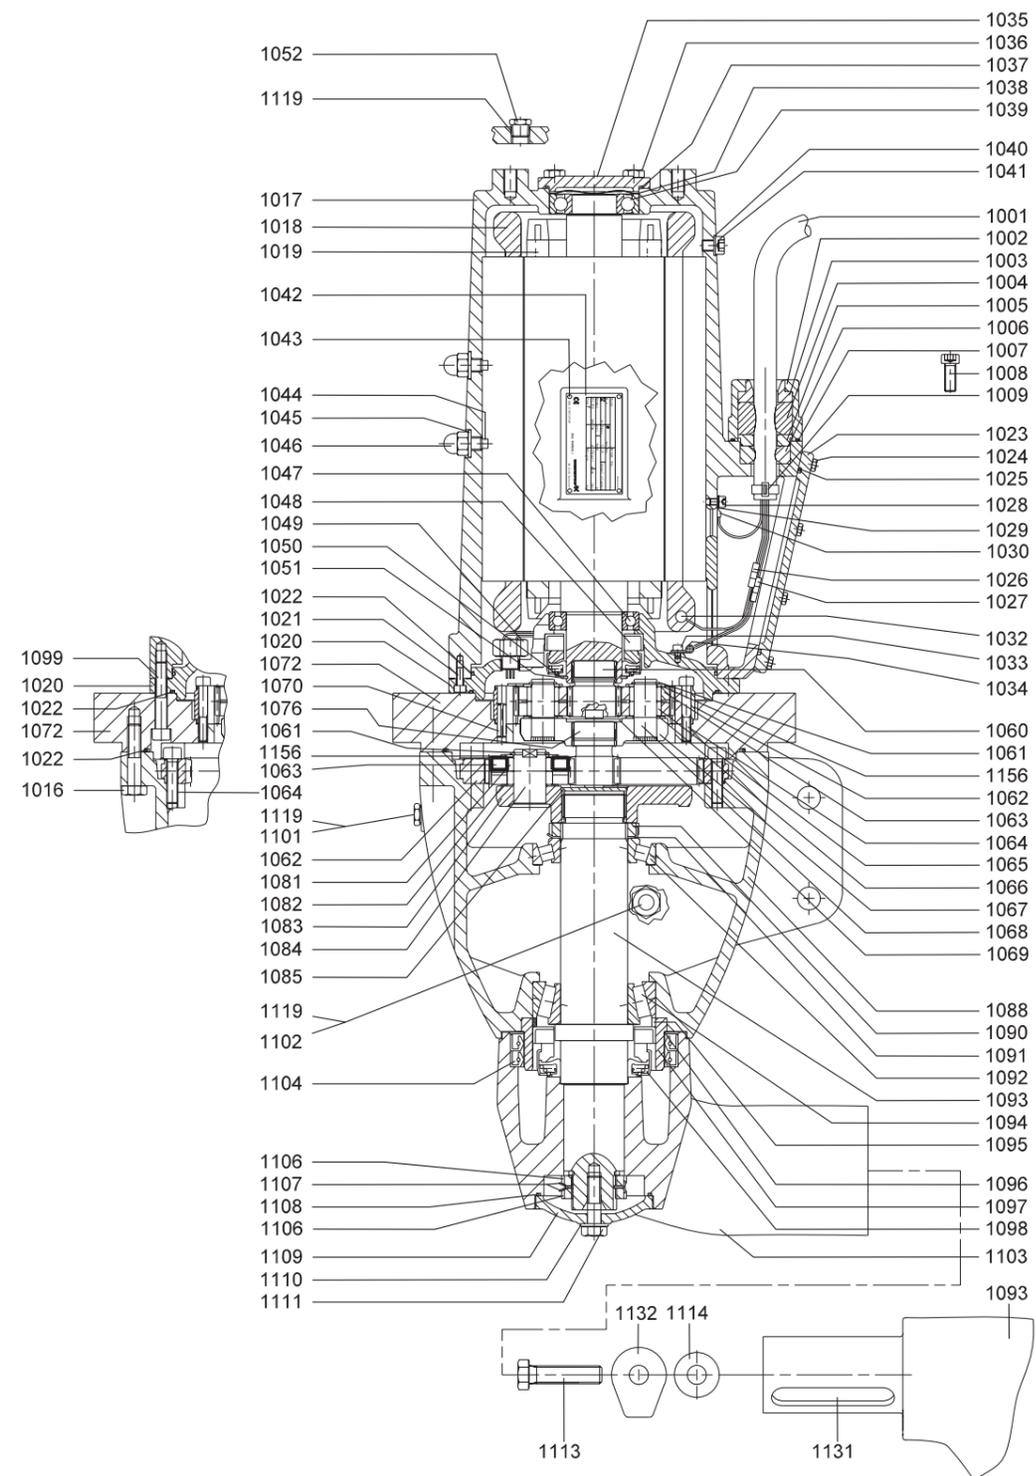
Чертеж в разрезе, AFG xx.260.xx
